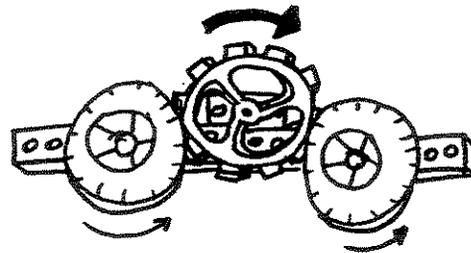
Desenho a mão livre do sistema de engrenagens
